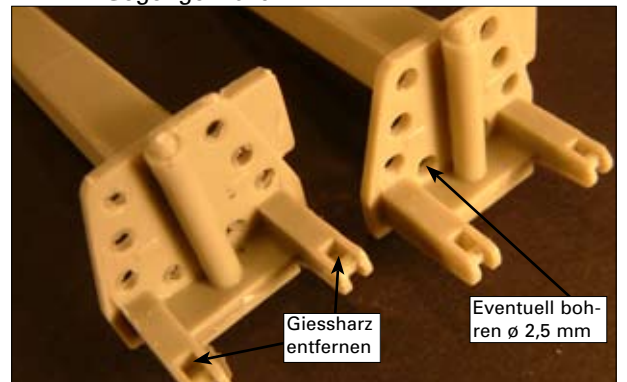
Unbearbeitetes neben einem bearbeiteten Ausleger
